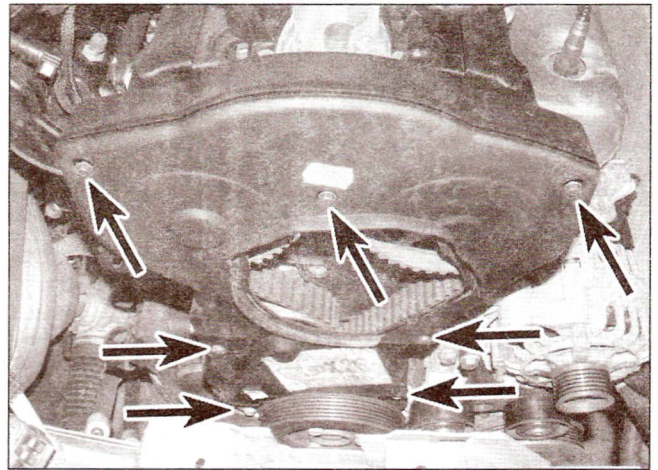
Болты крепления верхней крышки ремня газораспределительного механизма (отмечены стрелками)
